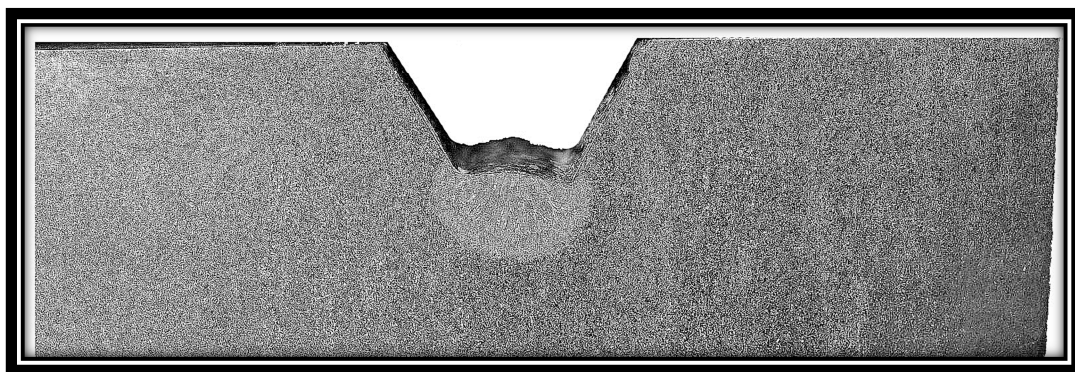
Detail TOO při obloukovém svařování obalenou elektrodou ϕ 2,5
